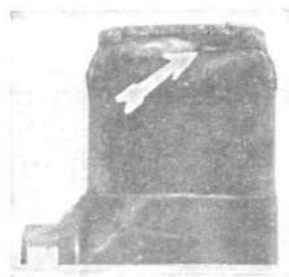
Незаполнение разделки при автоматической аргоно-дуговой сварке с присадкой.
